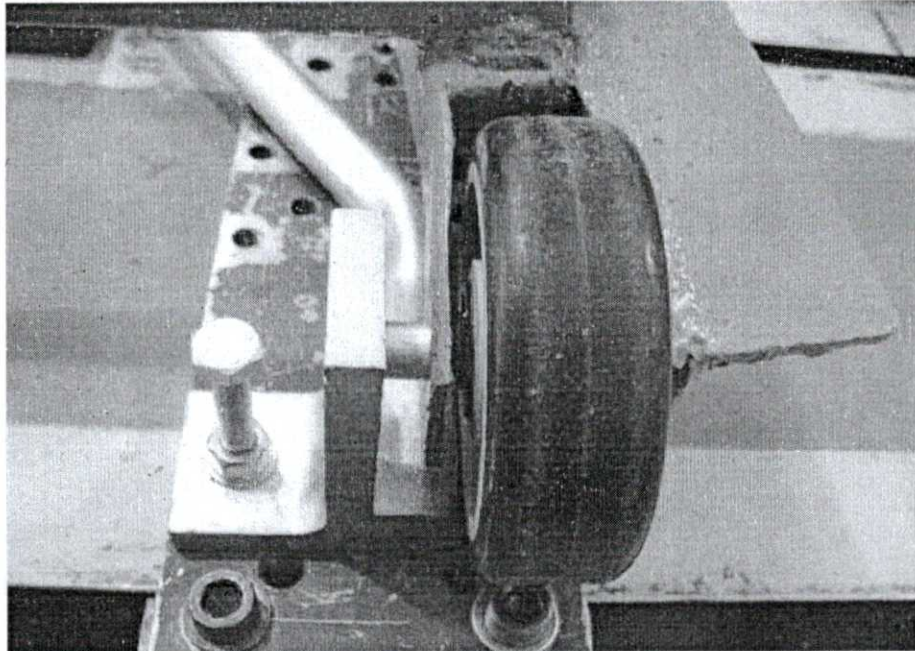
Lado esquerdo da amostra 1 após ensaio.
